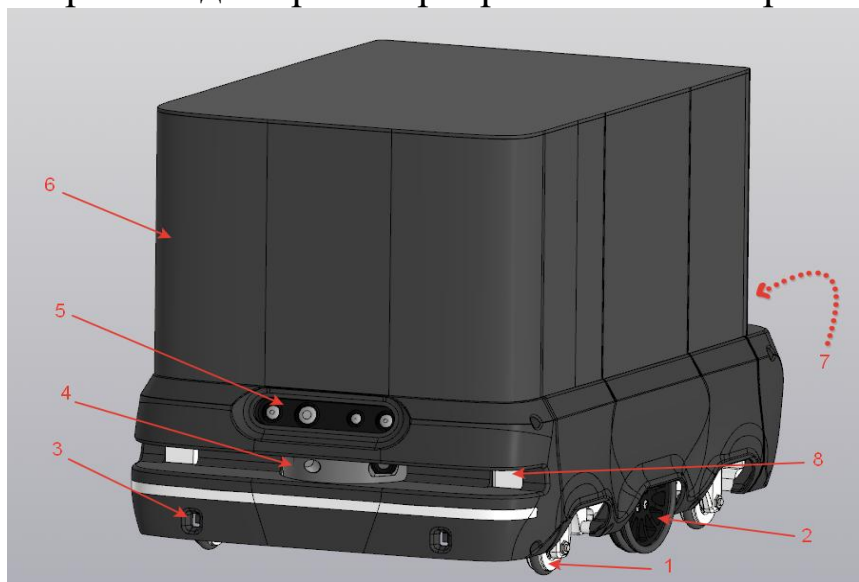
Мобильный колёсный робот для доставки посылок: 1 - опорные колёса;
